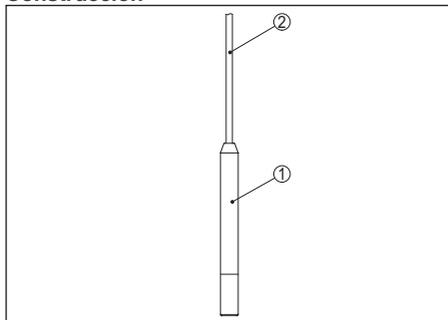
Construcción de la sonda de nivel tipo LH-20
